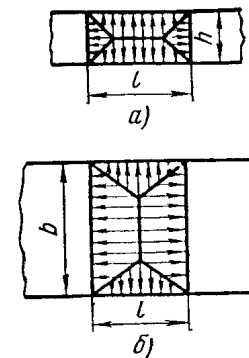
Схема деформации (находящегося между бойками объема металла) в плане: а — длинный очаг, б — широкий очаг; b — ширина заготовки, l — длина бойка
